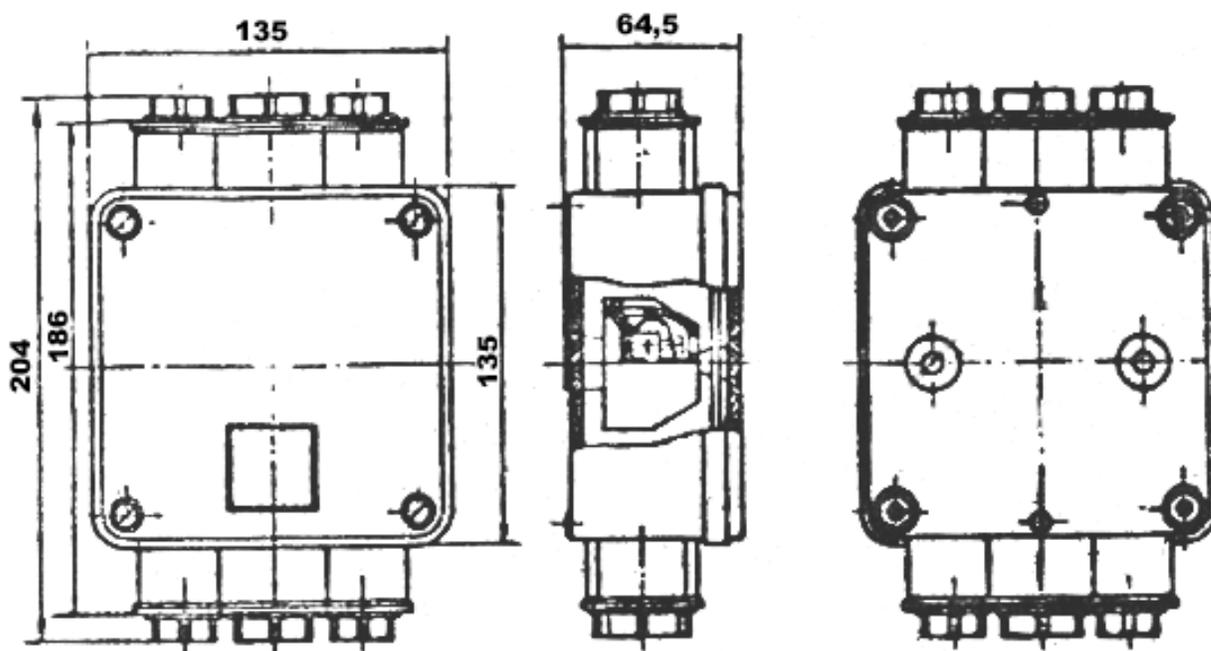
Коробка соединительная пластмассовая КСП10
